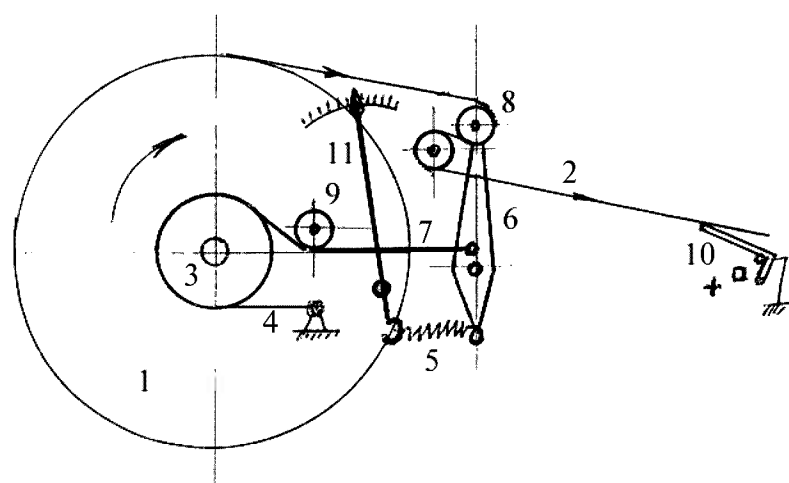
Схема устройства регулировки натяжения ленты: 1 — бумажный ролик; 2 — лента; 3 — тормозной шкив; 4 — стальная лента; 5 — пружина; 6 — коромысло; 7 — стержень; 8 — направляющий ролик; 9 — ролик; 10 — автомат для остановки машины; 11 — рычаг для регулировки натяжения
